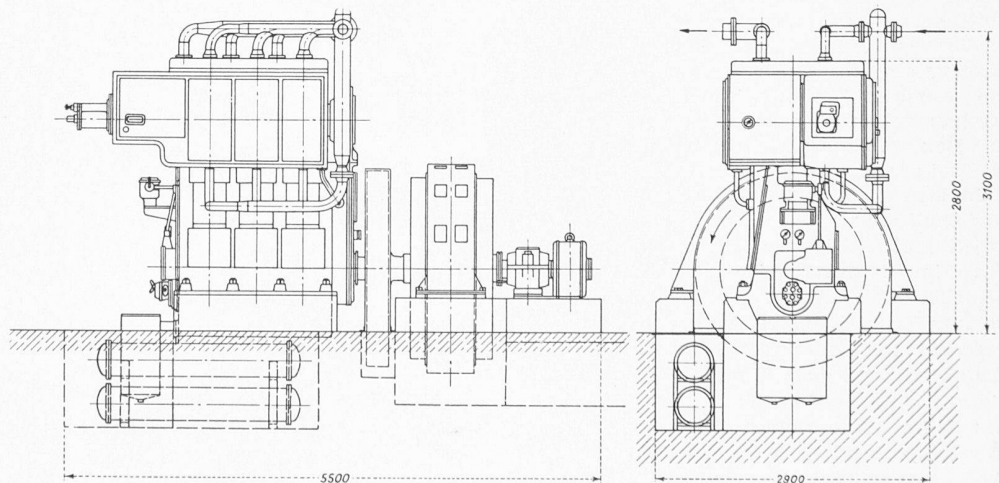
Typenskizze einer Dreizylindermaschine mit Generator 780 kW
